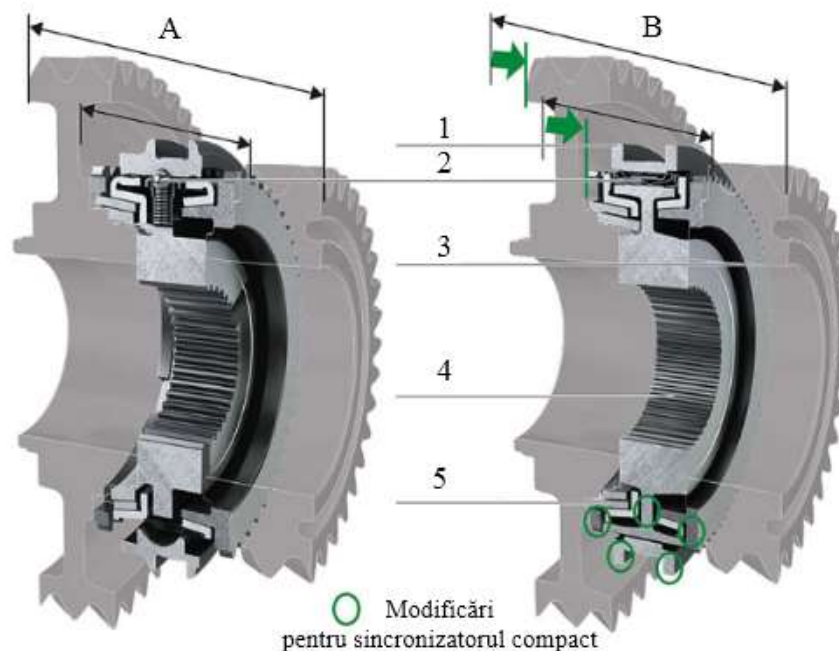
Sincronizatorul compact Schaeffler [75].
